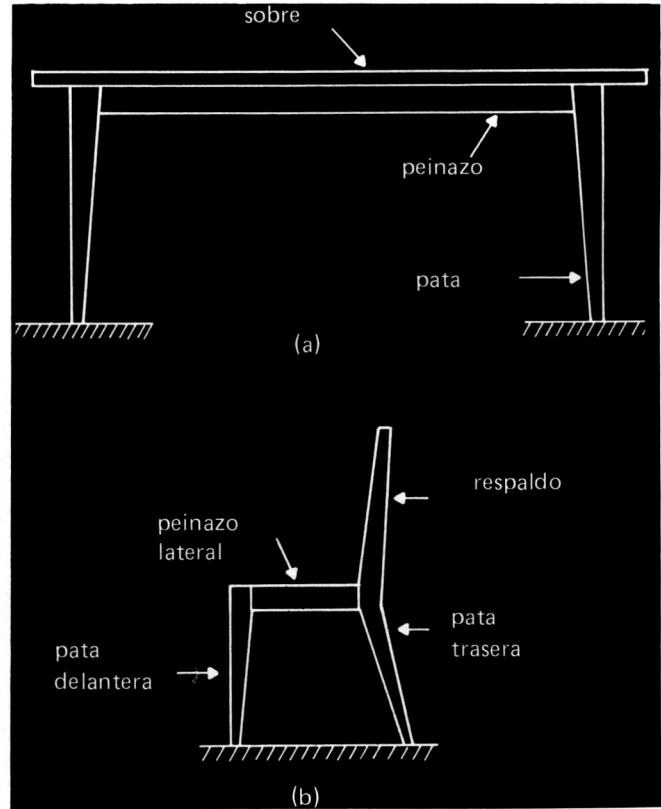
Sistema de construcción tipo armadura rígida de tres miembros. En la figura de mesa (a) se ha colocado un miembro adicional (peinazo). Este sistema también es utilizado en la construcción de sillas (b).
